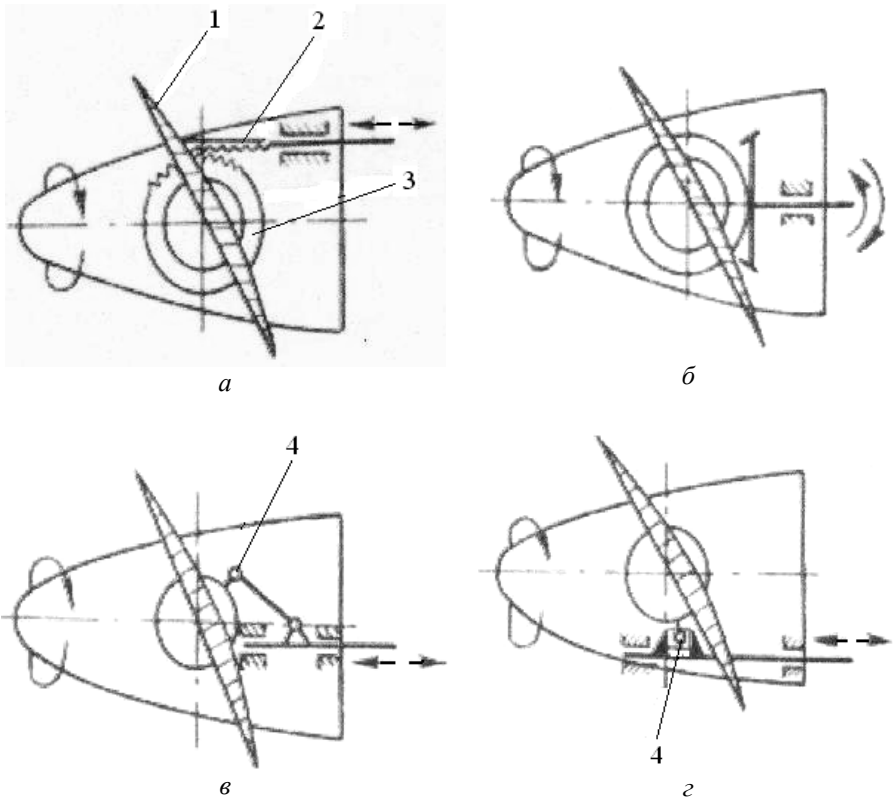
Кінематичні схеми гвинта з поворотними лопатями:
